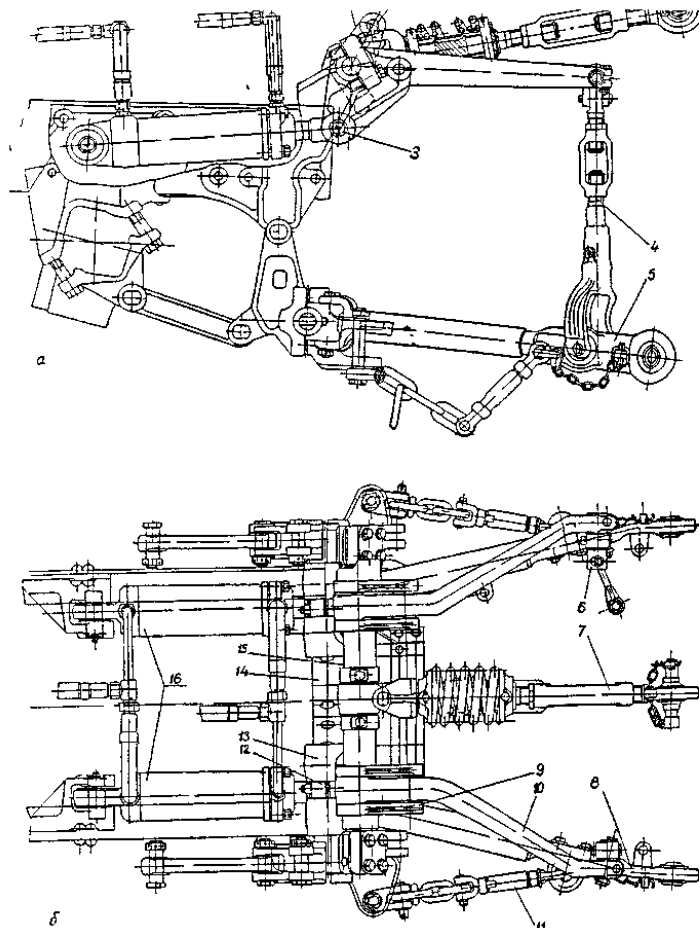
Схема конструкції навіски трактора: а – боковий вигляд; б – вид зверху; 1 – кронштейни стійок; 2 – стрижні стійок; 3 – палець штока; 4, 11 – регулювальні тяги; 5 – нижня тяга; 6 – фіксатор; 7 – верхня тяга; 8 – кріплення ланцюга; 9 – опорна шайба; 10 – верхня тяга; 12 – шток гідроциліндра; 13 – втулка; 14, 16 – вали важелів.
